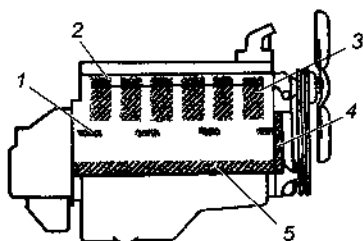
Зоны прослушивания двигателя для определения дефектов различных деталей: 1 — клапанов; 2 — поршневых пальцев, шатунных подшипников; 3 — распределительных зубчатых колес; 4 — коренных подшипников; 5 — подшипников распределительного вала
